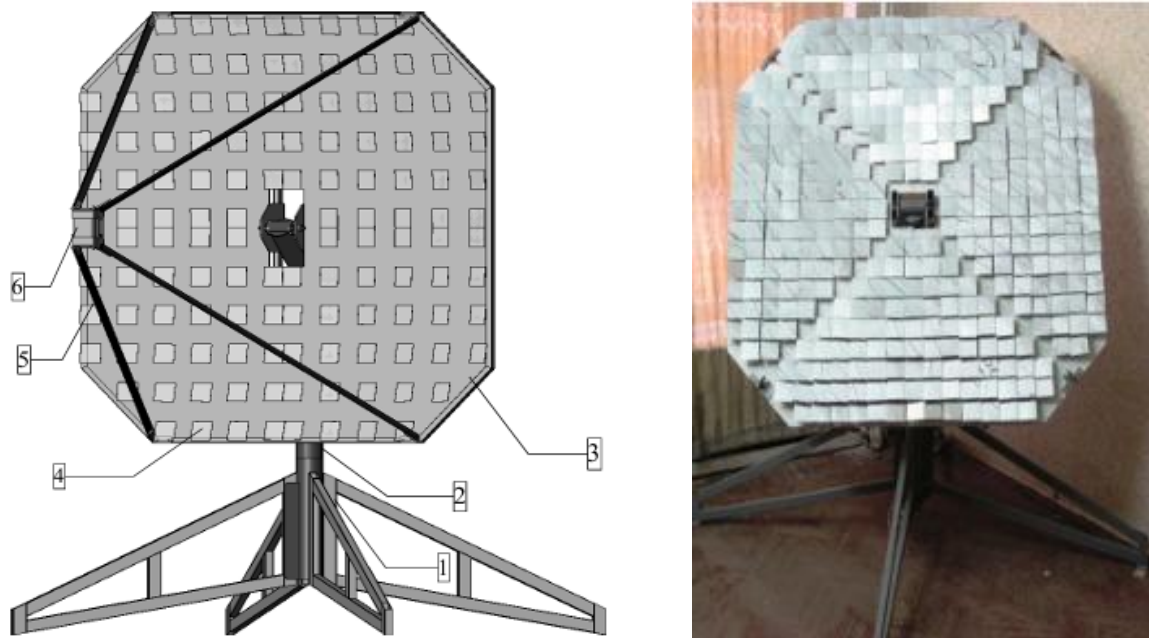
Загальний вигляд експериментального зразка фотоенергетичної установки [7]: 1 – основа з чотирма опорами, підшипниковими вузлами для вертикальної осі обертання, редуктором та азимутальним приводом; 2 – поворотна частина з механізмом нахилу, підшипниковими вузлами для горизонтальної осі обертання; 3 – несуча конструкція концентратора; 4 – елемент концентратора – орієнтоване дзеркало (показано приблизно 30 % усіх дзеркал); 5 – стрижні підвісу фотоенергетичного блока; 6 – фотоенергетичний блок
